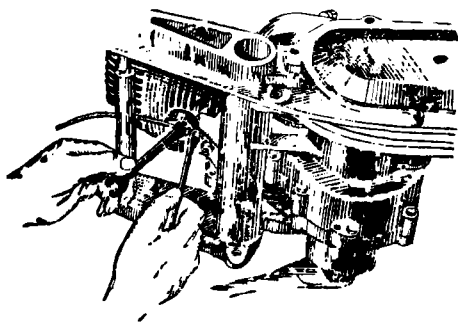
Регулировка натяжения троса управления сцеплением упором на корпусе задней подвески
